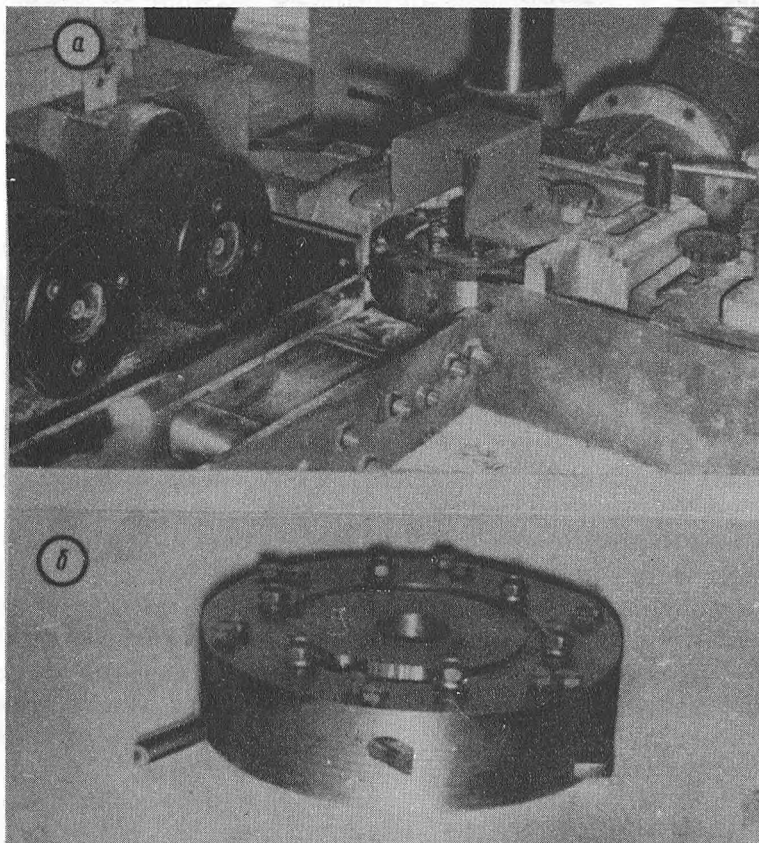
Общий вид узла резания и подачи опытной установки (а); фреза с винтовым расположением вставок из СТМ (б).
